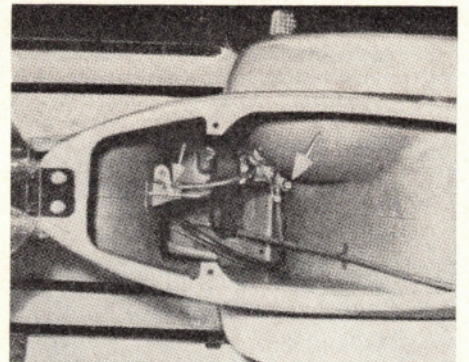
Linker Pfeil: Hier wird der Starterzug ausgehängt; rechter Pfeil: Die Schraube für den Klemmring.
